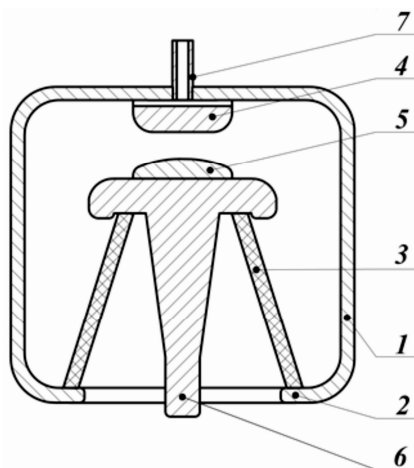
Базовая конструкция разрядника-обострителя (1 – корпус, 2 – отбортовка корпуса, 3 – изолятор, 4 – анод, 5 – катод, 6 – вывод, 7 – штенгель)
